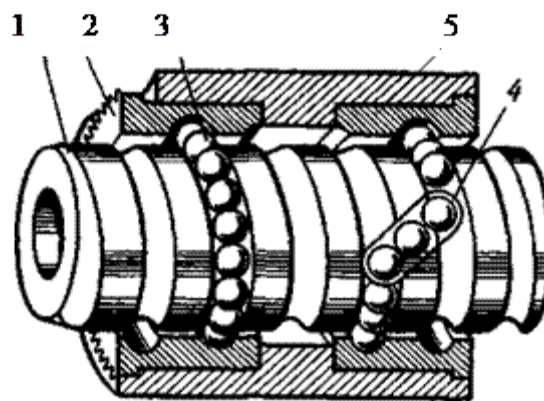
Конструктивна схема передачі гвинт-гайка кочення: 1 - гвинт; 2, 5 – гайки з канавками; 3 – кульки; 4 – канал повернення кульок.
